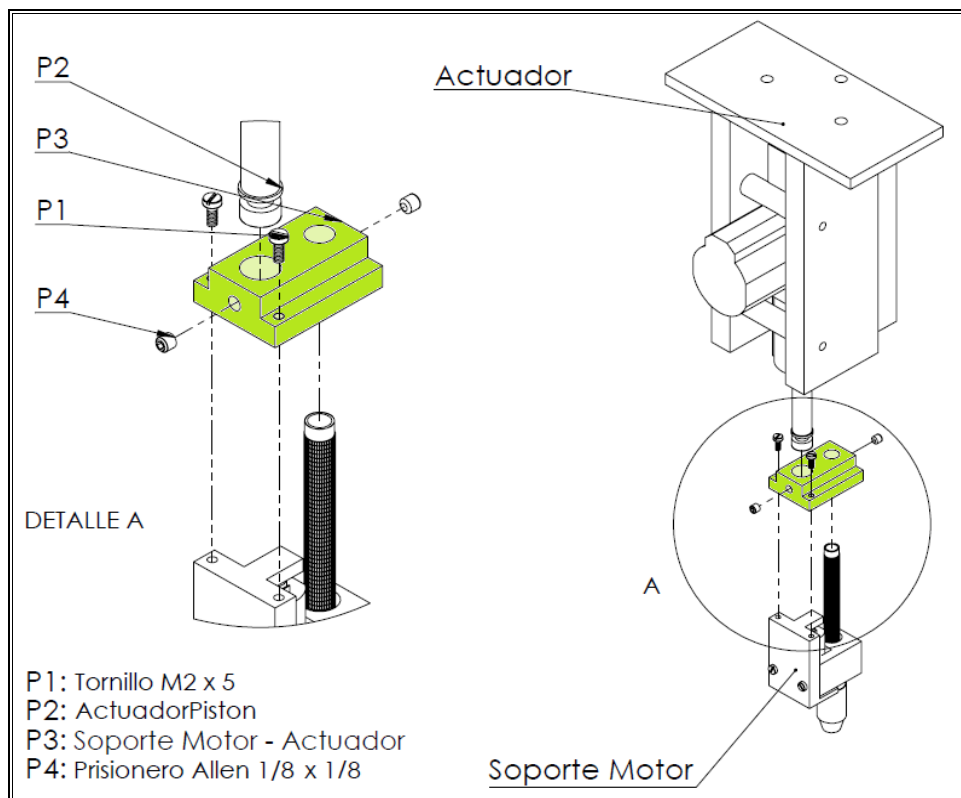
Dibujo de subensamble de uno de los mecanismos del sistema de Inserción de hilo, utilizando la pieza Soporte Motor – Actuador resaltada en verde. Se distingue a su vez el pistón del Actuador y el Soporte de motor.
